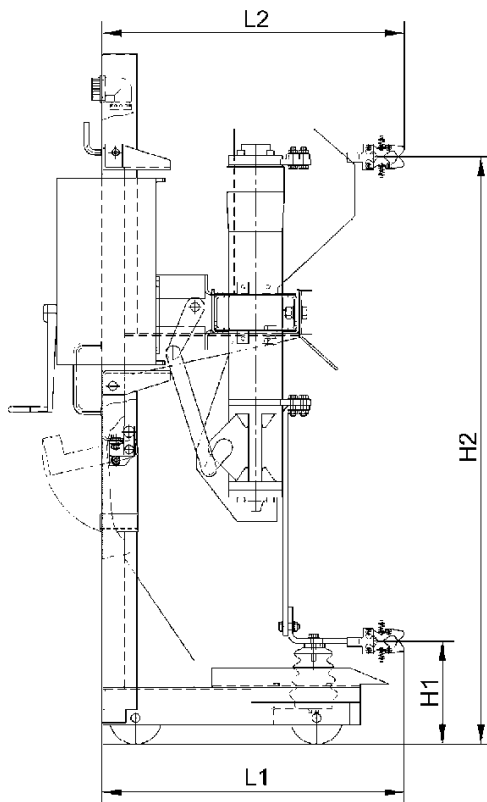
Положення штепсельних роз'єднувальних контактів фрагментів шин зі встановленими верхніми ШРК
